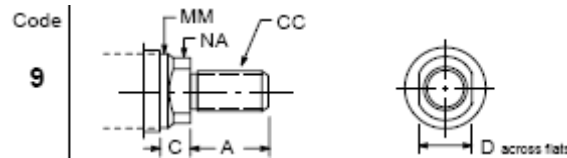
Dimensiones del final de vástago código 9, para cilindro compactador principal.
